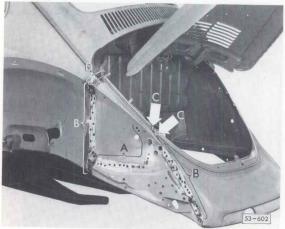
Seitenteil-Auschnittsteil, Motorabdeckblech und Auschlußblech hinten einschweißen.
